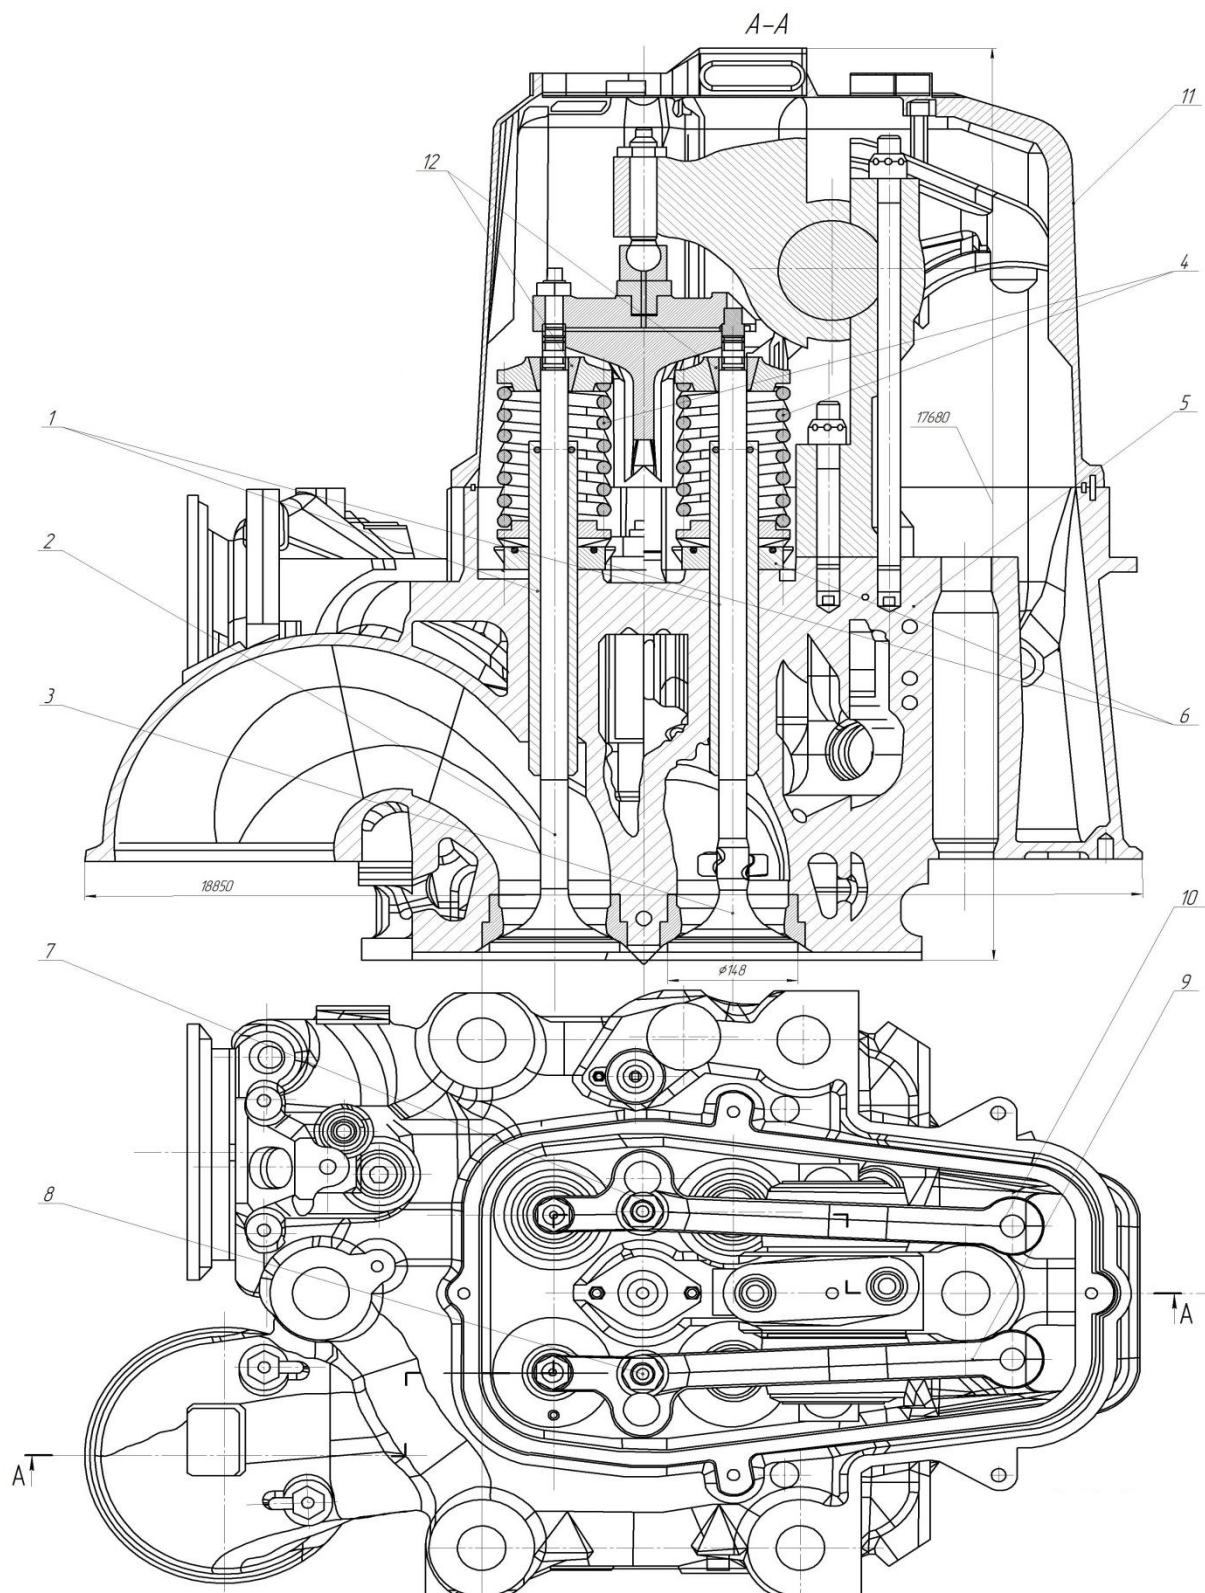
Компонування деталей газорозподільного механізму у головці циліндра суднового двигуна Мак 8М43С: 1 – втулка клапана; 2 – впускний клапан; 3 – випускний клапан; 4 – пружина; 5 – корпус головки циліндрів; 6 – механізм повороту клапана; 7 – комплект випускного клапана; 8 – комплект впускного клапана; 9 – рокер впускного клапана; 10 – рокер випускного клапана; 11 – кришка головки циліндра; 12 – затискний конус
